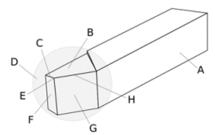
Ferramenta de usinagem destinada ao torneamento.
